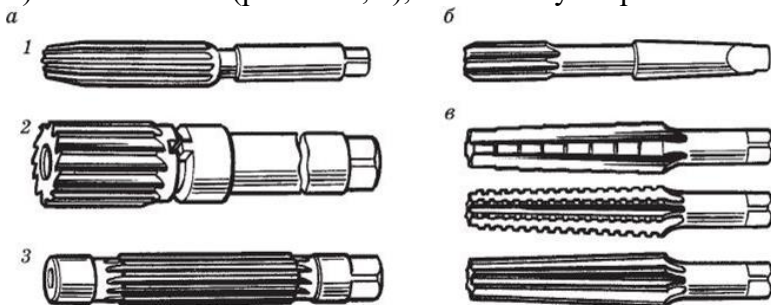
Типы разверток: а — цилиндрические ручные (1 — с прямым зубом; 2 — цилиндрическая насадная; 3 — регулируемая); б — машинная; в — комплект ручных конических разверток
